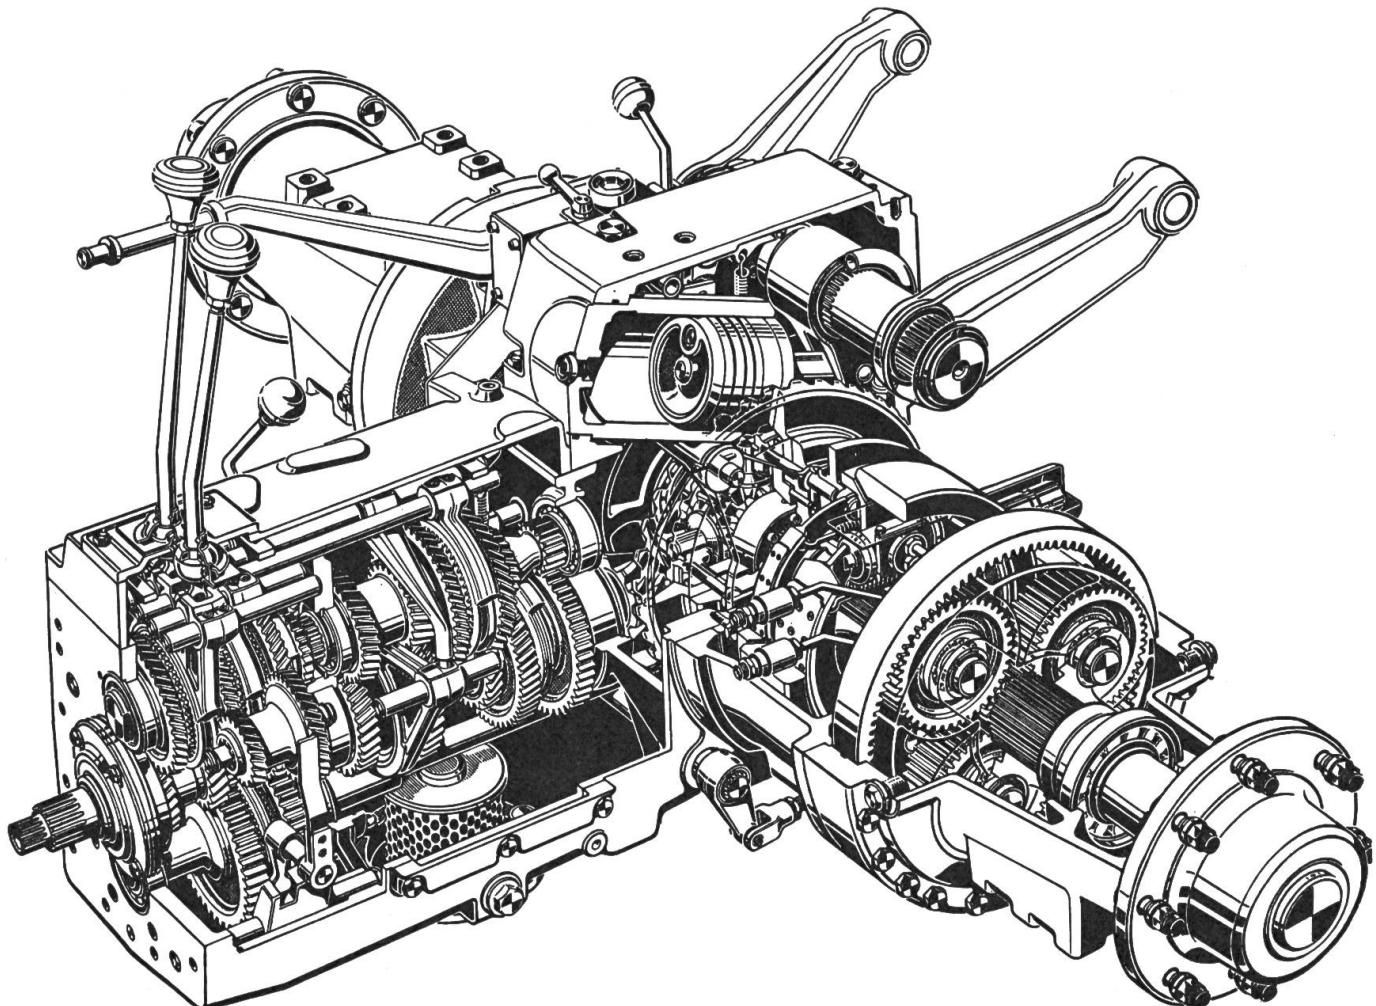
Coupe d'un changement de vitesse typique y compris les commandes auxiliaires de l'essieu arrière et de l'installation hydraulique — Dessin ZF Friedrichshafen, RFA.
